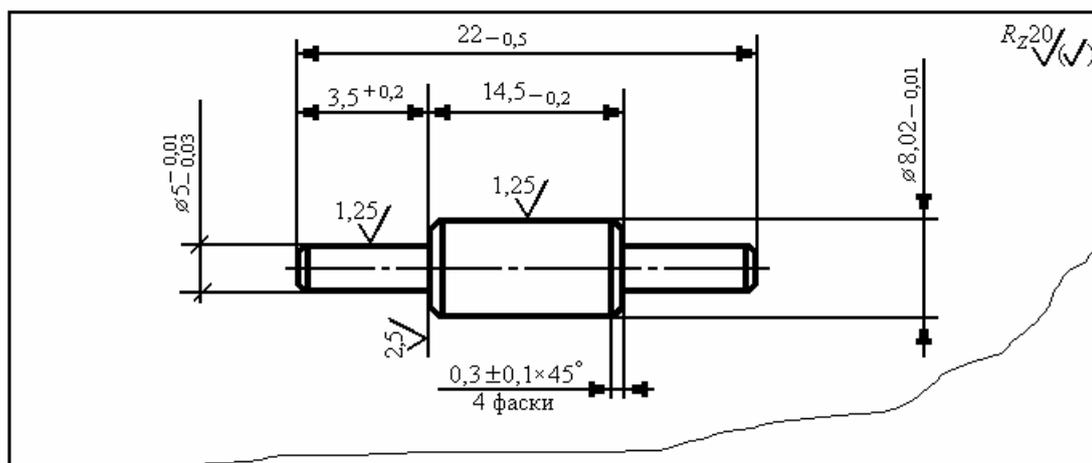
Вариант обозначения на чертеже значений шероховатости поверхностей
